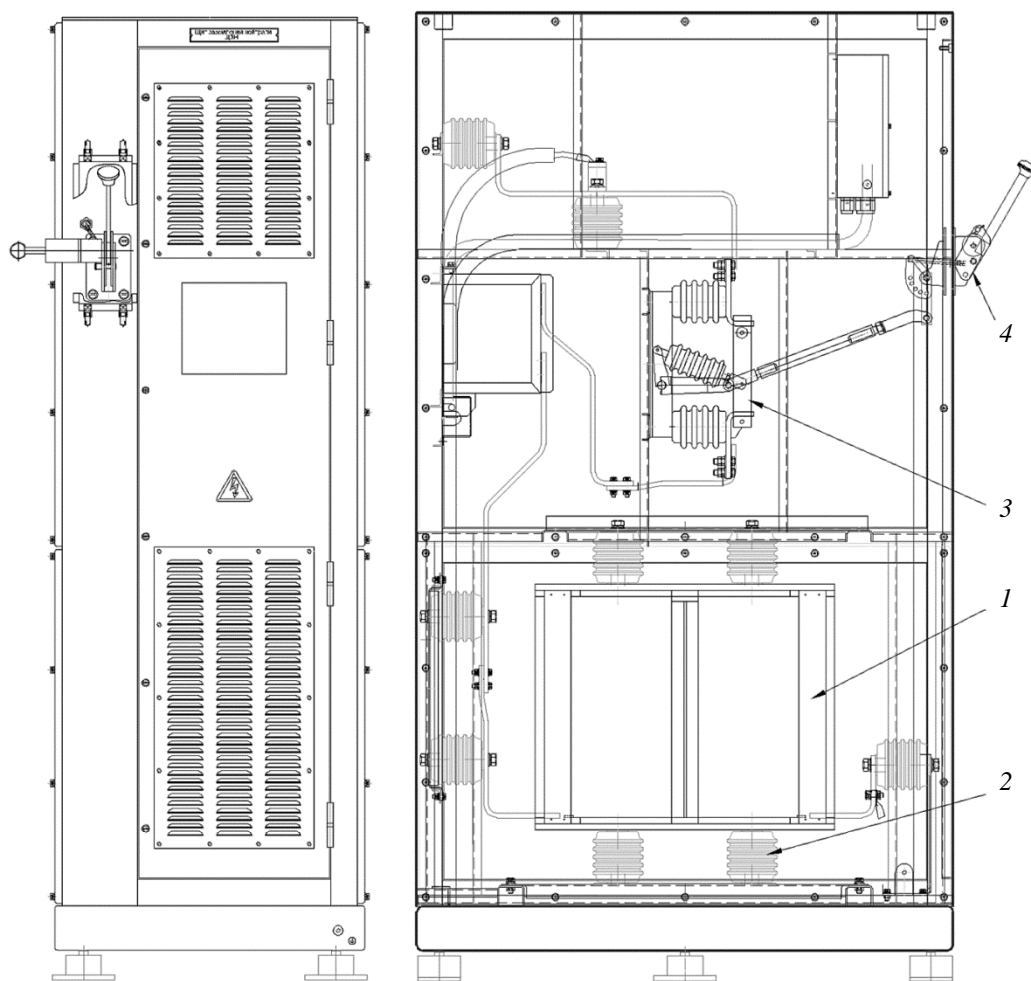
Общий вид щита заземления нейтрали: 1 – резистор P31; 2 – изолятор ИОР-10-7,5; 3 – разъединитель РЛВОМ; 4 – ручной привод ПР-10А
